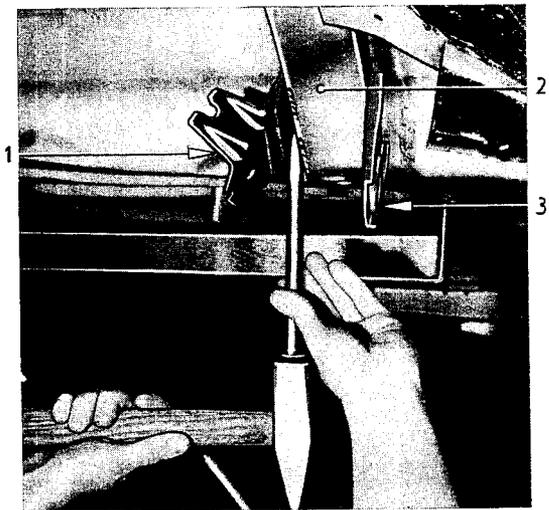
Untere Schweißpunkte an innerer Stütze bei nach innen gebogener Stütze trennen
